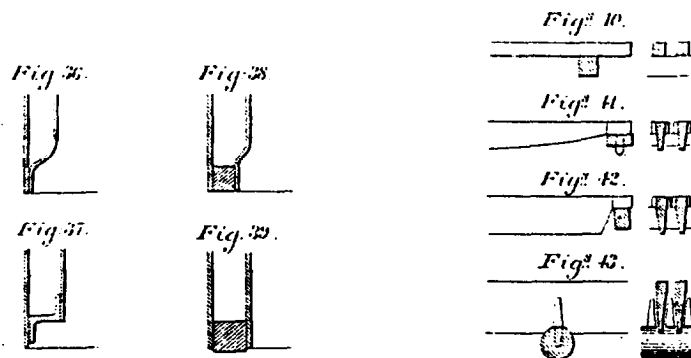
à 43. — Évolution du cadre du foyer et de la grille.
